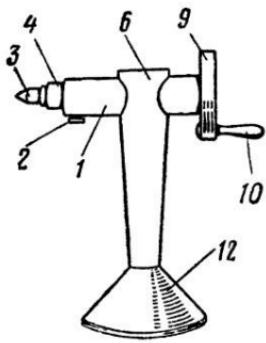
Модель задней бабки токарного станка: 1 — консоль; 2 — стопорный винт; 3 — центр; 4 — пиноль; 6 — стойка; 9 — диск; 10 — ручка; 12 — основание.
